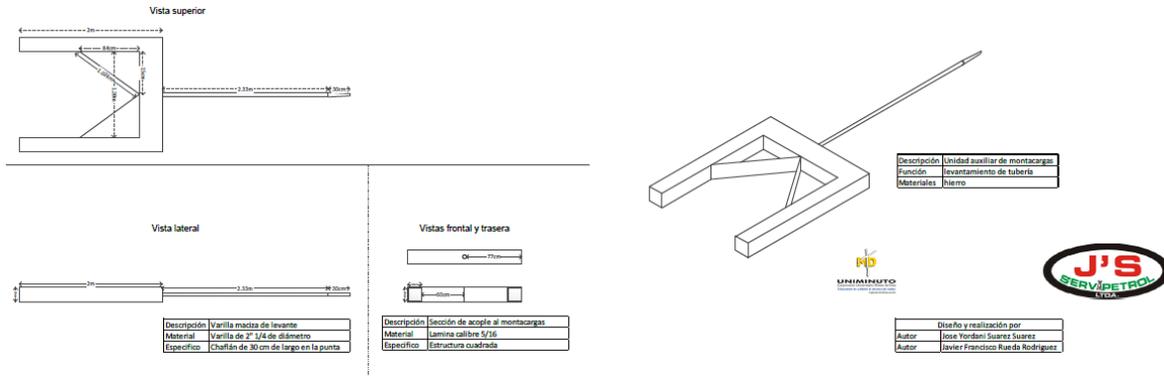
PLANO COMPLETO. Fuente: Autoría propia
